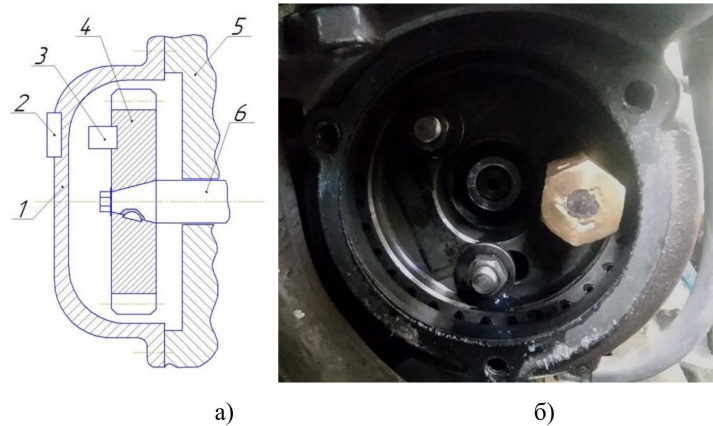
Вузол датчика моменту вприскування активатора і швидкісного режиму: а) монтажна схема; б) місце установки датчика на дизелі; 1 – передня кришка ТНВД; 2 – датчик Холла; 3 – неодимовий магніт; 4 – приводна шестерня паливного насоса; 5 – корпус паливного насоса; 6 – вал приводу паливного насоса.
